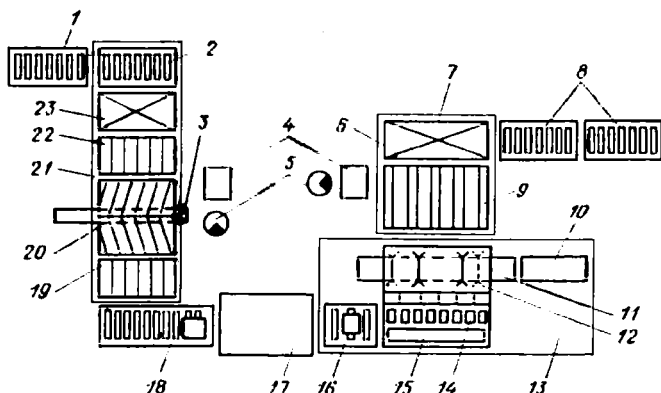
Линия чистовой обработки заготовок модели ДПД60-7
